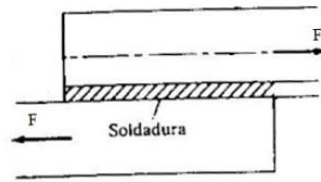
Soldadura de filete con esfuerzos de corte en el área efectiva.
